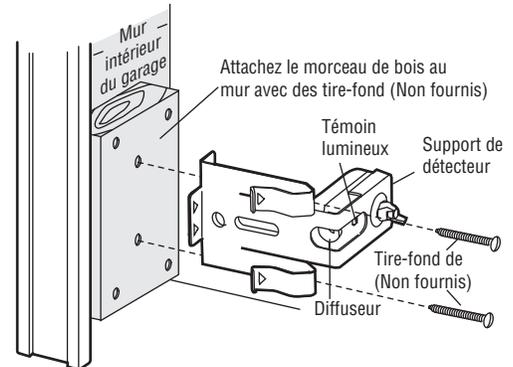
MONTAGE MURAL (CÔTÉ DROIT)
